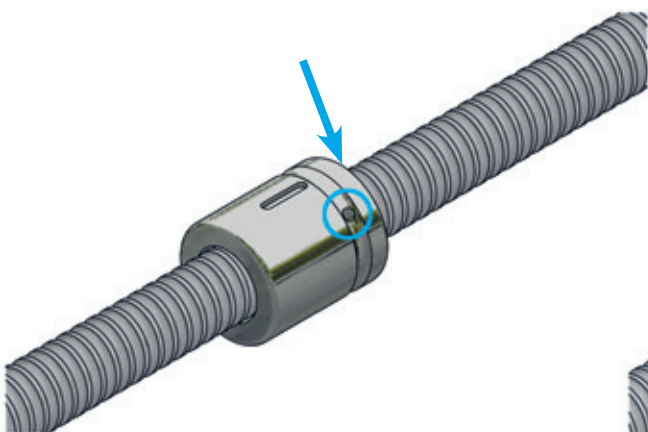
Zylindrische Mutter mit Schmierbohrung
